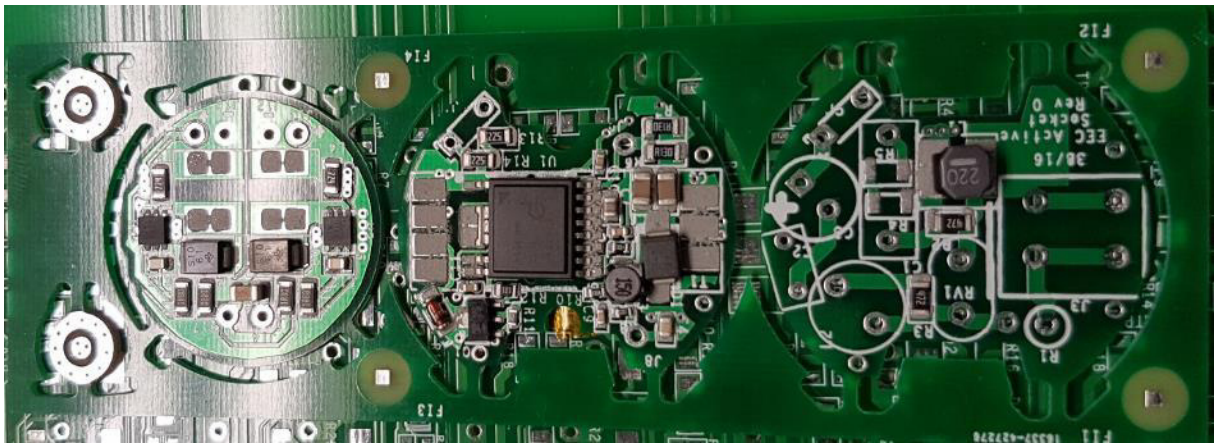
PCB em fase inicial da soldadura dos componentes SMD
